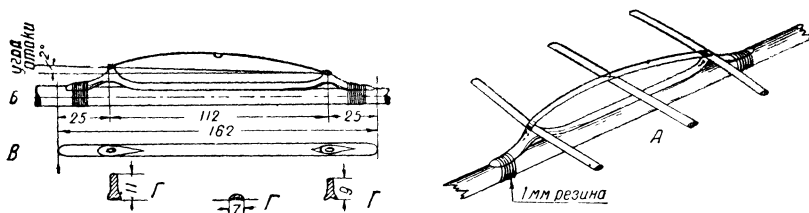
Крепление крыла: А — общий вид крепления; Б — вид крепления сбоку; В — вид передней планочки крепления сверху; Г — сечение передней планочки крепления крыла
